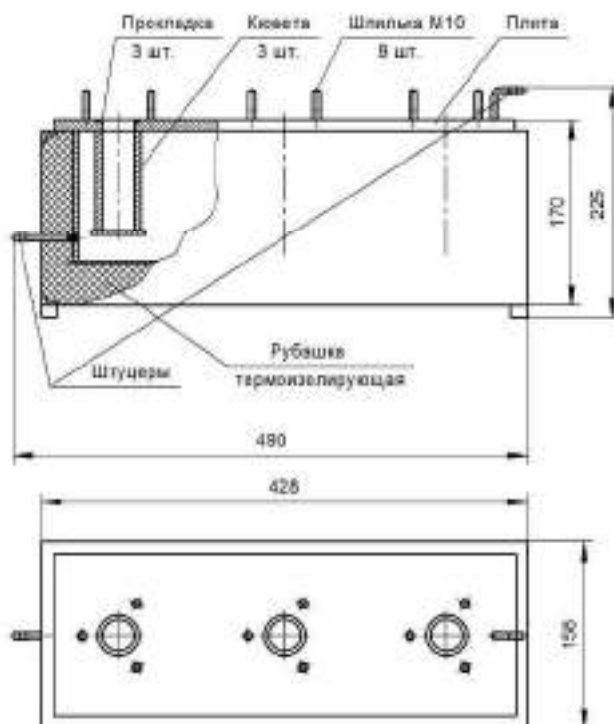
Внешний вид и габаритные размеры приспособления П1-01
